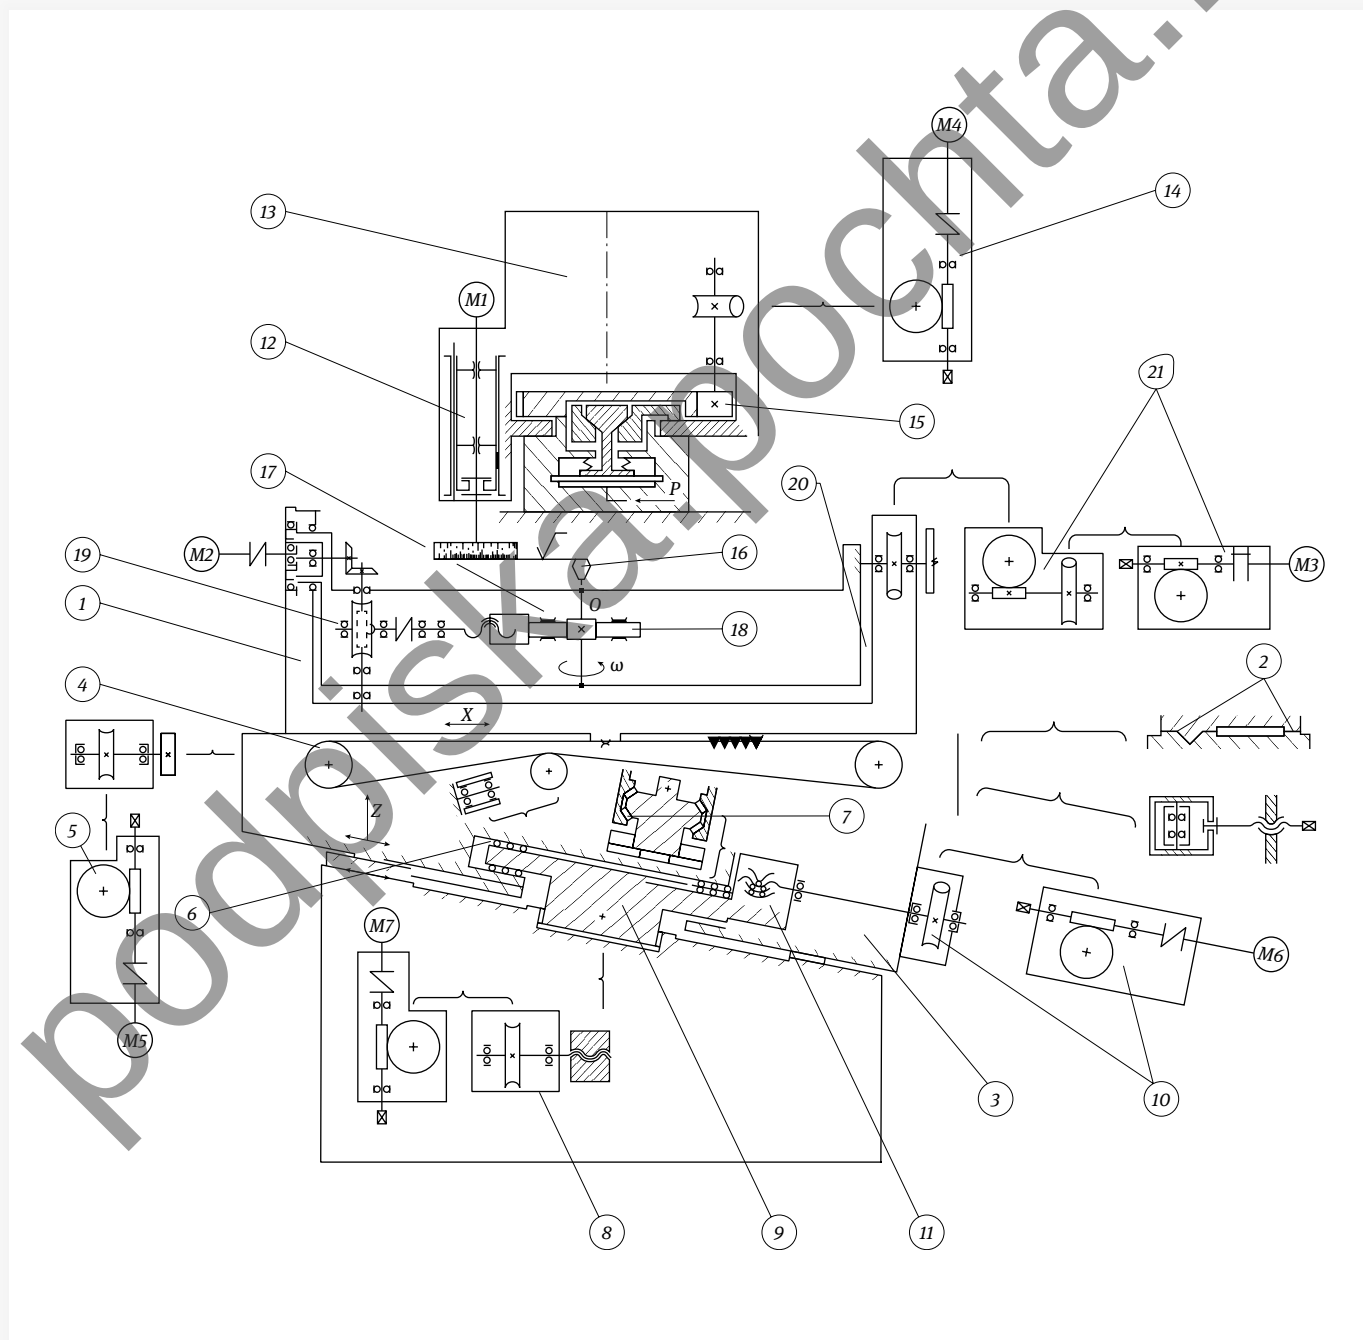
Кинематическая схема станочного модуля АН15Ф4 с ЧПУ
